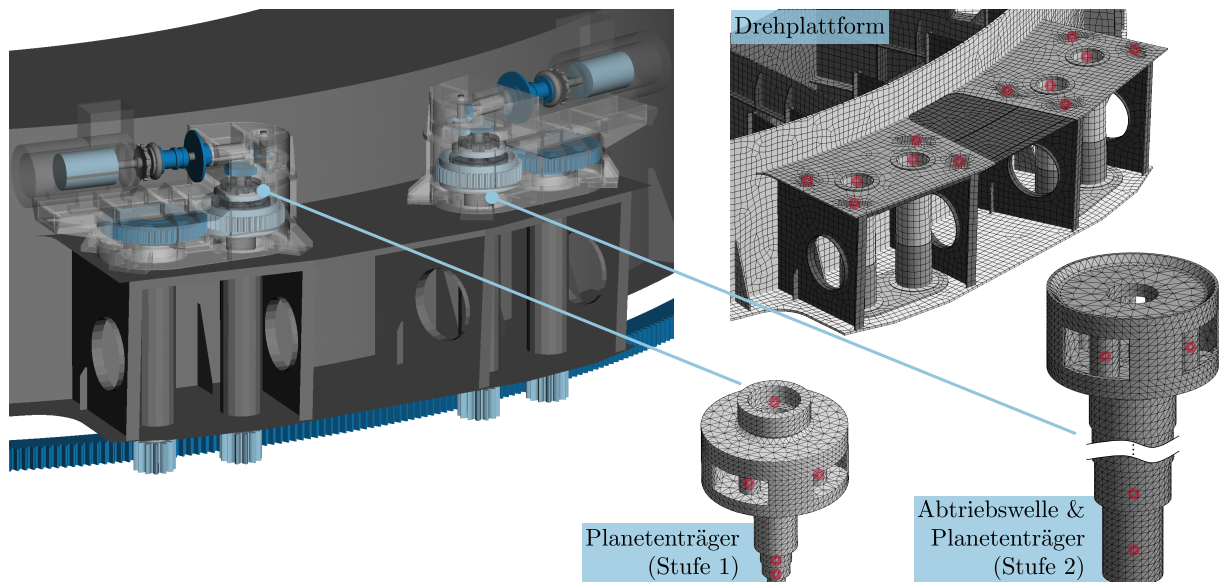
Zwei Einzelantriebe des Schwenkwerkes montiert auf der Drehplattform des Baggeroberbaus und Detaildarstellungen ausgewählter flexibler Körper
